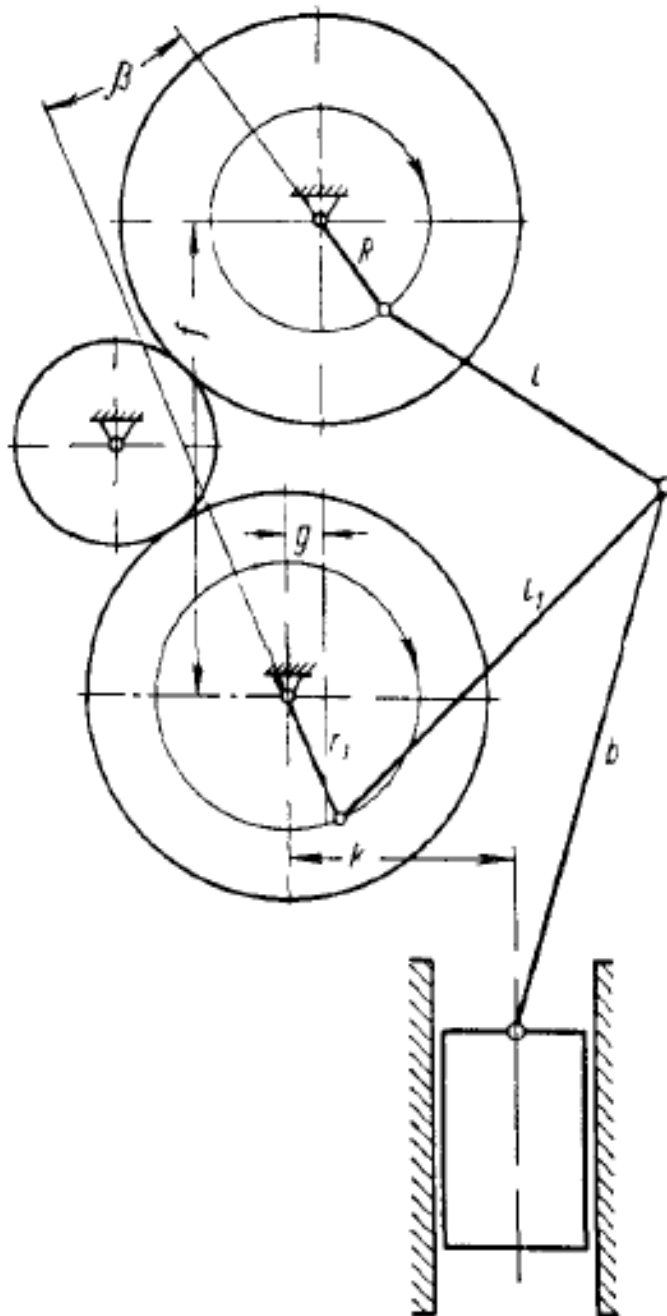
Схема семиланкового механізму з двома ведучими кривошипками
